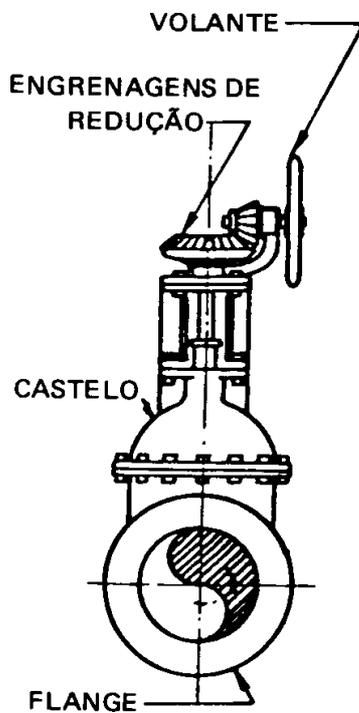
Válvula de gaveta, pequena com redução de engrenagens.
